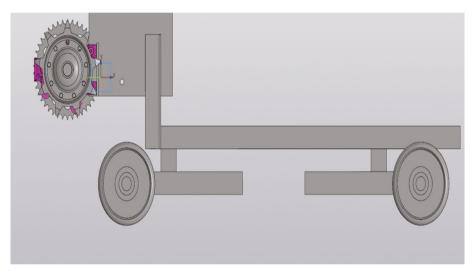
Гусеница с ведомой звездочкой и опорными катками
